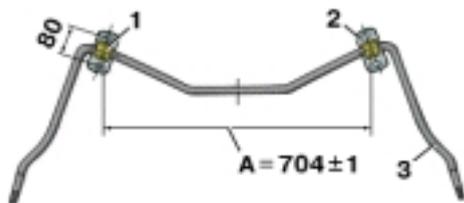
Установка скоб стабилизатора: 1 – подушка; 2 – скоба; 3 – штанга
